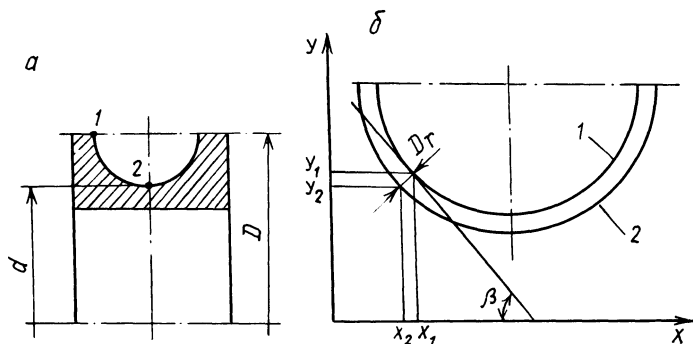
К определению неравномерности съема металла с различных участков профиля: а – профиль обрабатываемой детали; б – схема измерения
